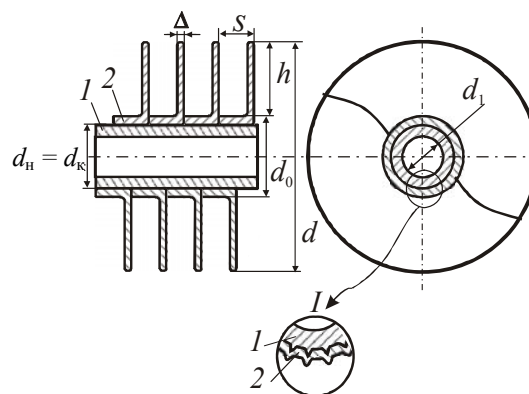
Конструкция биметаллической ребристой трубы с навитыми спиральными KLM-ребрами: 1 – несущая труба; 2 – KLM-ребра
